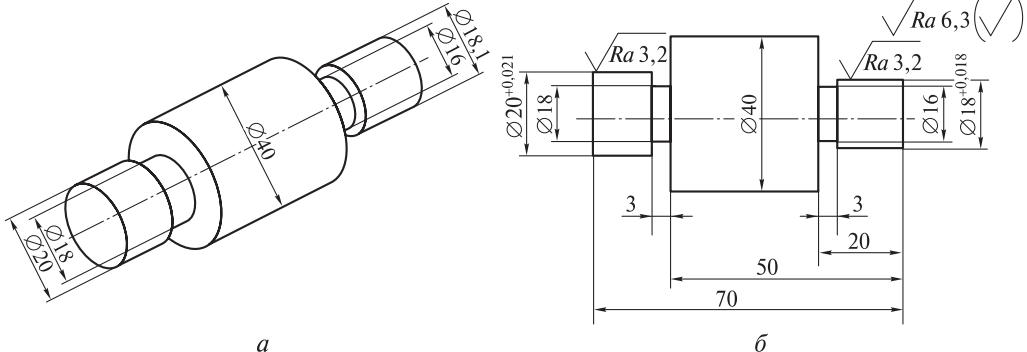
Изображение (*a*) и чертеж (*б*) детали «вал»
